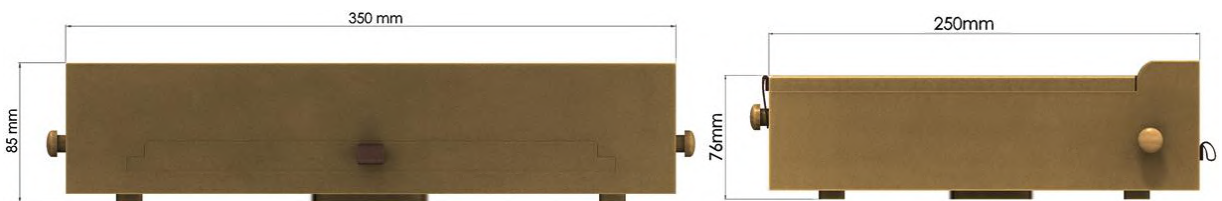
Dimensões gerais da prancheta Fonte: Elaboração própria
